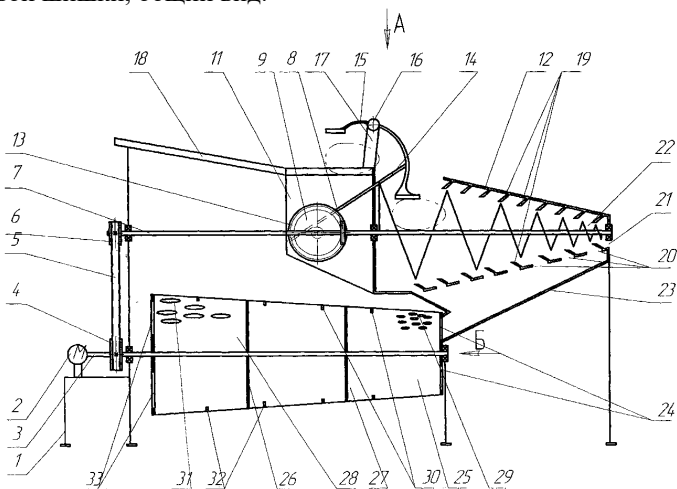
Устройство для извлечения ореха из кедровой шишки, общий вид
